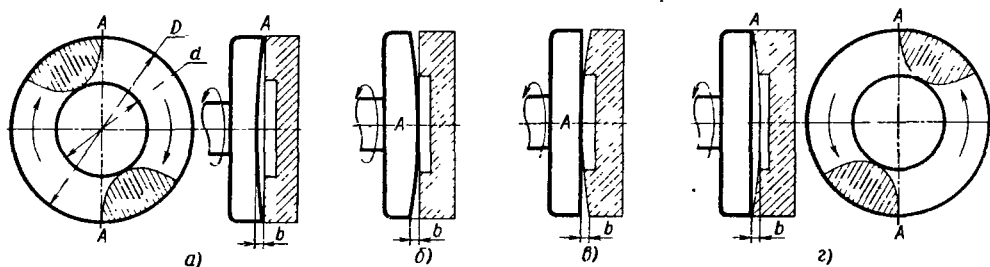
Двухклиновые опоры с цилиндрическими поверхностями
